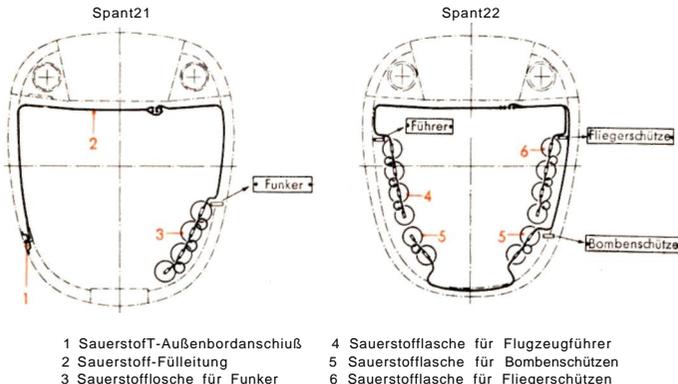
Spant 21 und 22 gegen Flugrichtung
